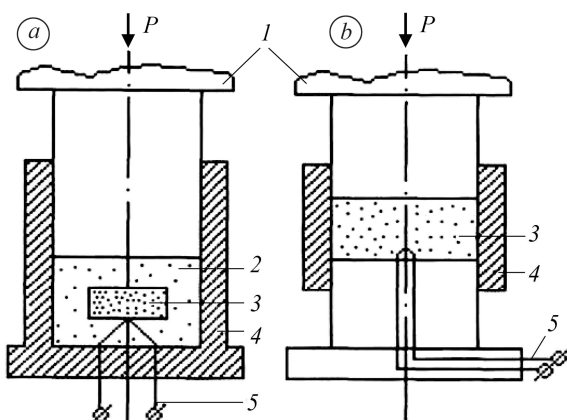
Принципові схеми термохімічного пресування для малих (a) та великогабаритних (b) заготовок: 1 – пуансон; 2 – теплоізолятор; 3 – шихта СВС; 4 – прес-форма; 5 – ініціувальний пристрій.
